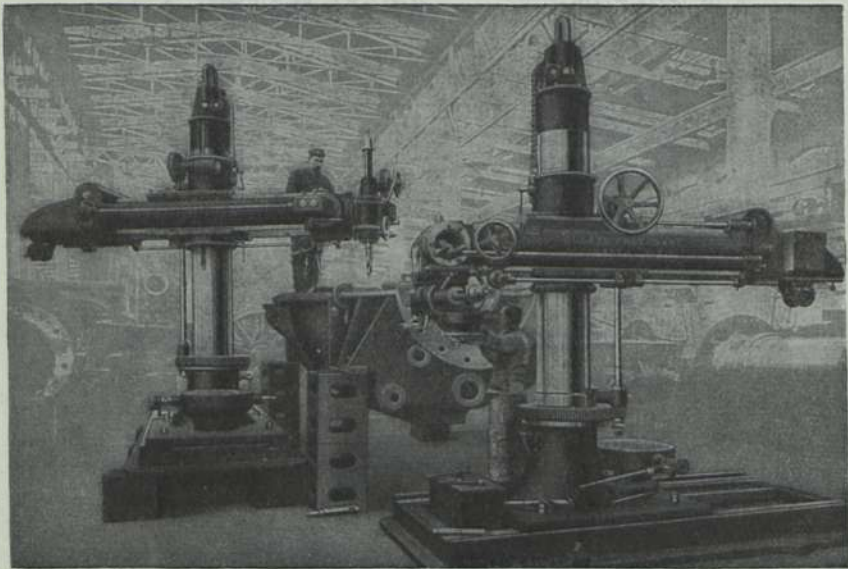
Tragbare Bohrmaschinen. Collet & Engelhard, Offenbach a/M.
